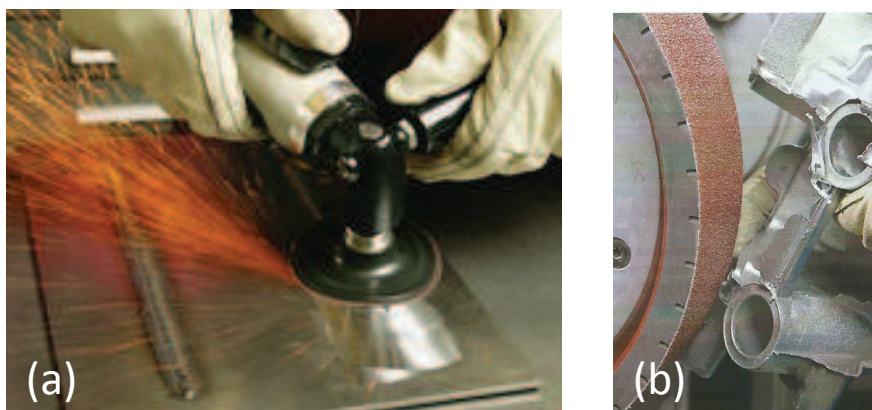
Opérations de reprise de forme - (a) arasage de soudure (b) ébarbage (source 3M, PFERD)
